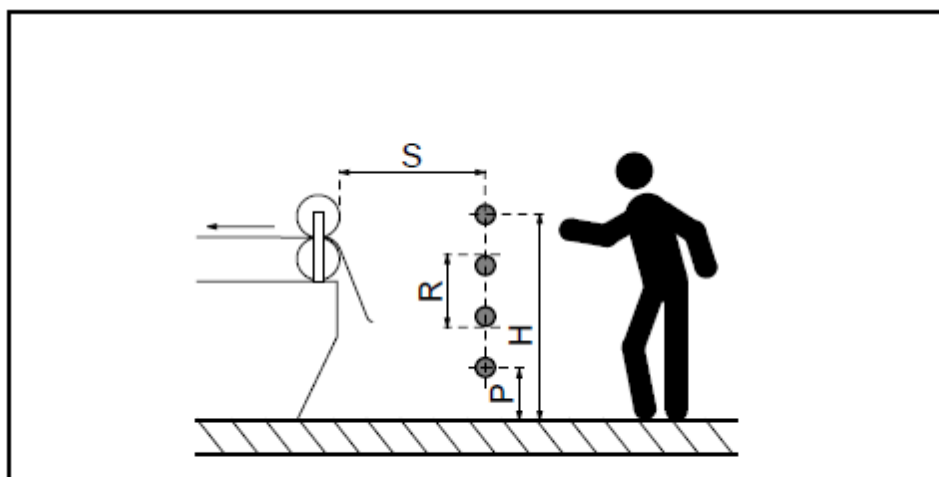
Barriera di sicurezza pluriraggio, direzione di avvicinamento perpendicolare
